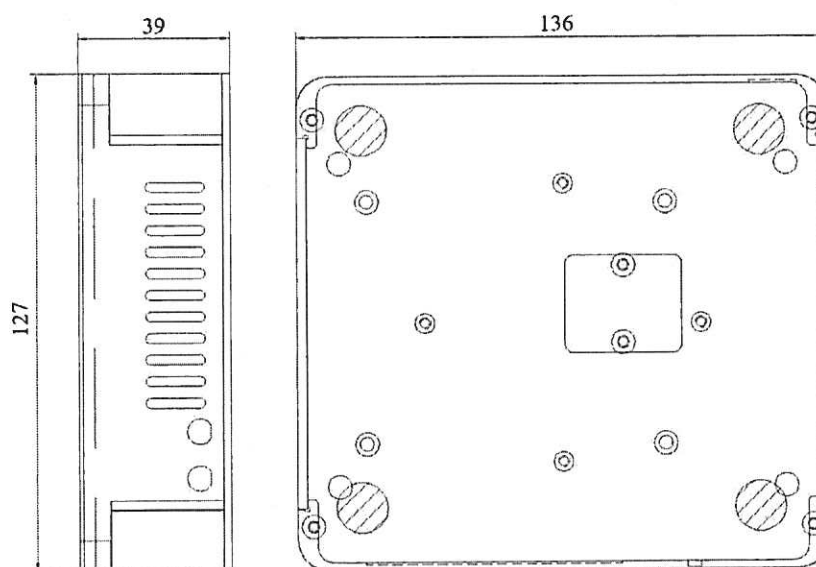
Внешний вид и габариты PCE-P-02-NSW (виды снизу и сбоку).
